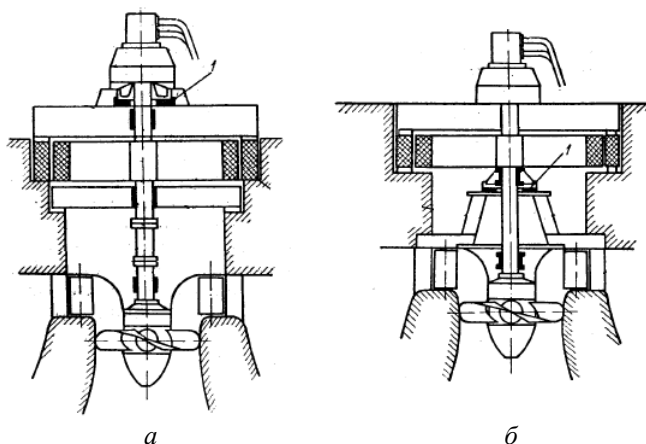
Компоновка вертикальных гидроагрегатов: 1 – подпятник
